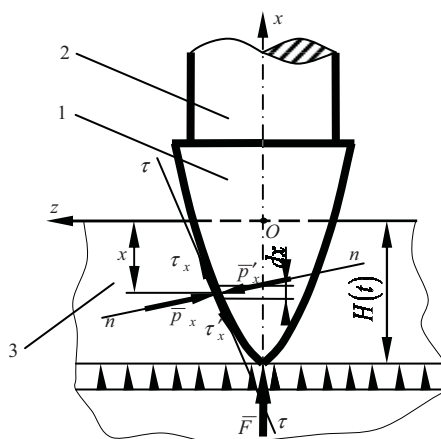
Расчетная схема очага f деформации в процессе прошивки трубной заготовки: 1 – оправка; 2 – стержень оправки; 3 – трубная заготовка
